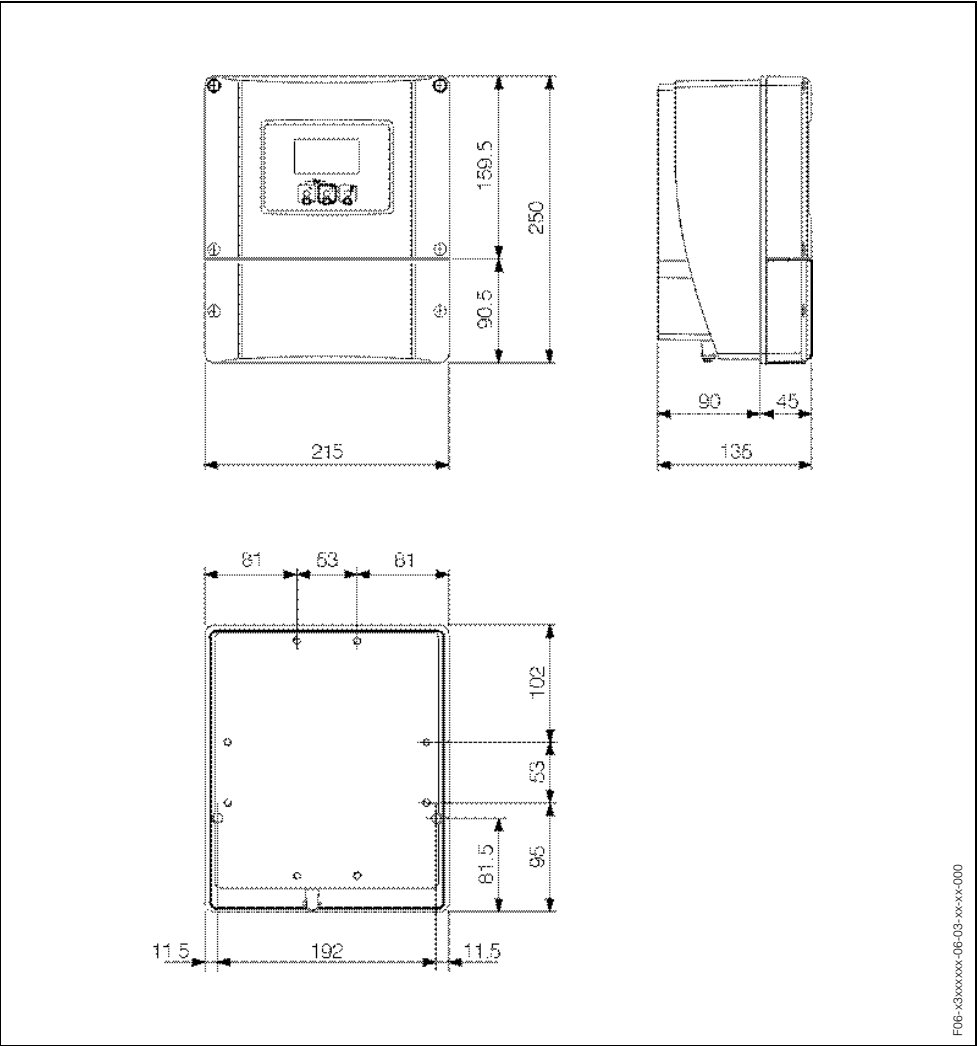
Dim. del cabezal para montaje pared (para la instal. con panel y el montaje adosado a la tubería → pág. 42)
